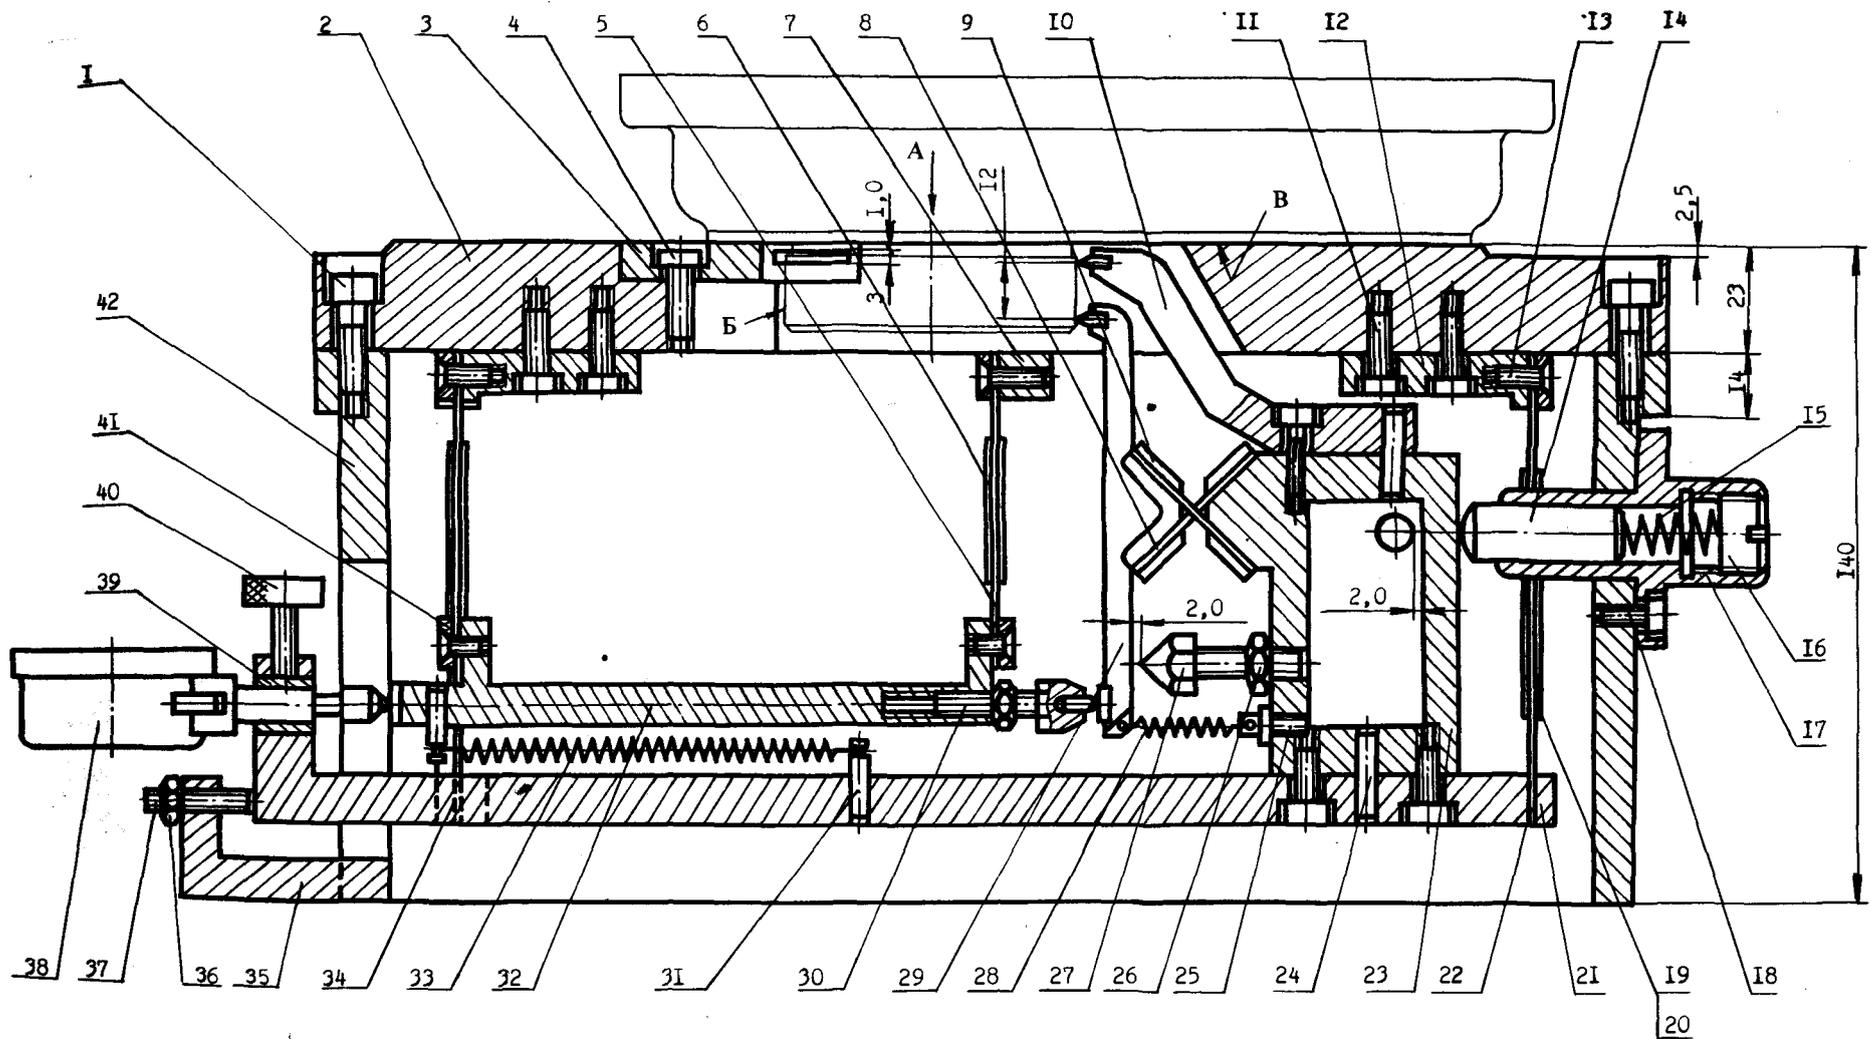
Контрольное приспособление для ступенчатого диска:
